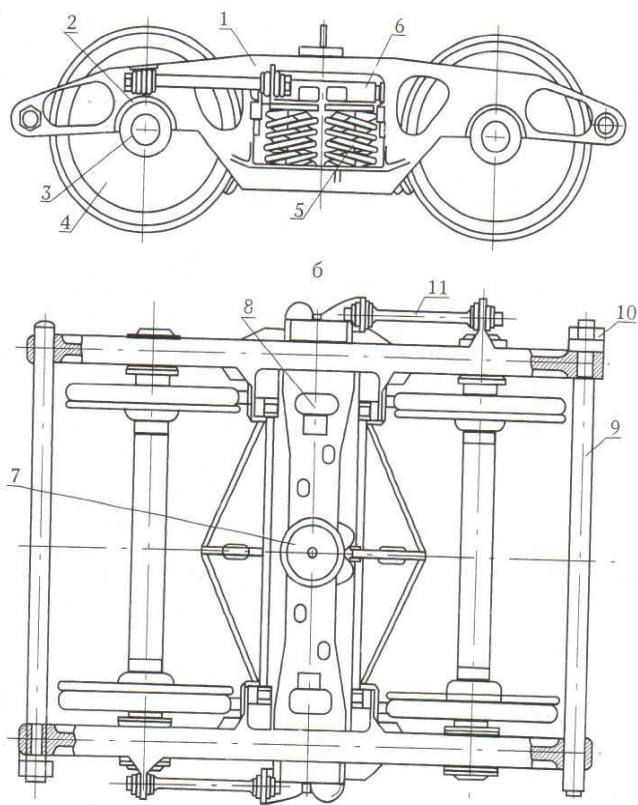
Візок типу 50.100: 1 – бокова рама; 2 – буксова прокладка; 3 – буксовий вузол; 4 – колісна пара; 5 – ресорний комплект; 6 – надресорна балка; 7 – підп'ятник; 8 – ковзун; 9 – стрижень; 10 – гайка; 11 – тягові повідки
